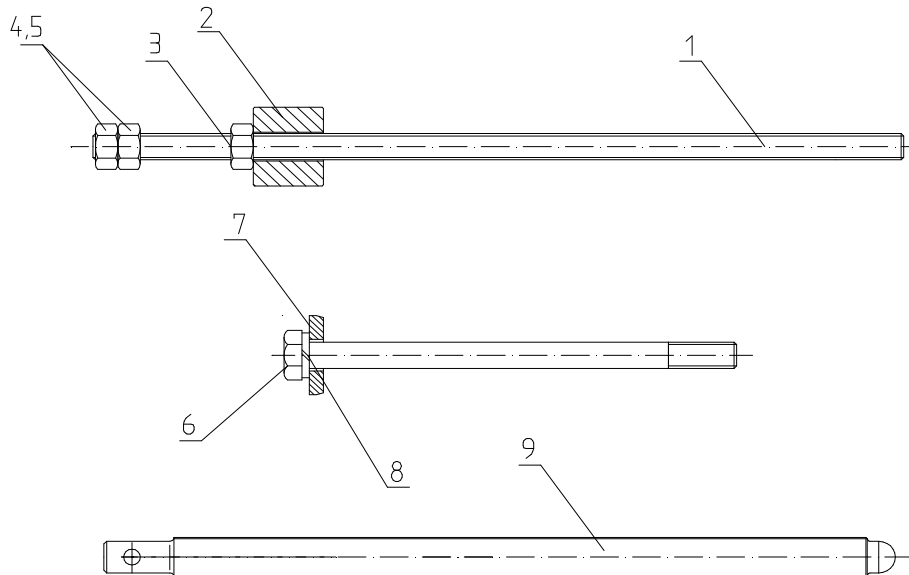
Vorrichtungen zur Montage, Befestigung und Demontage
